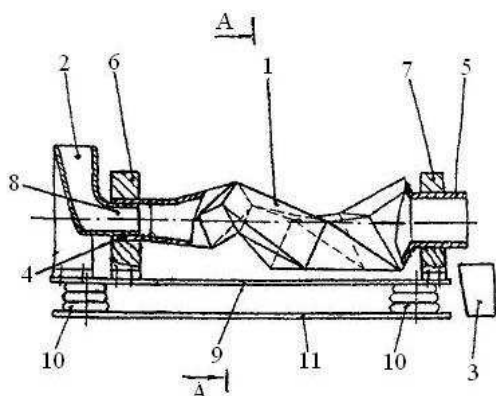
Устройство для смешивания сыпучих материалов, вид спереди
